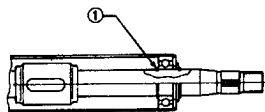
Верхний подшипник рулевой колонки и разрезное стопорное кольцо (установите стопорное кольцо (1) перед установкой вала) (См. Раздел 16)
